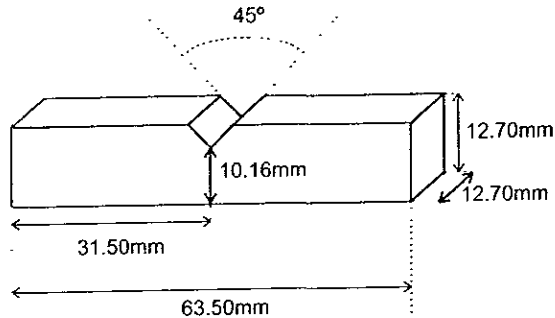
Dimensiones del espécimen para la prueba de impacto.
